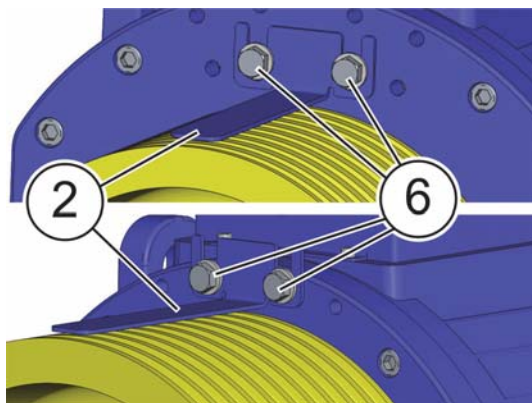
Variantes de montage 3ème protection contre le rebond des câbles
